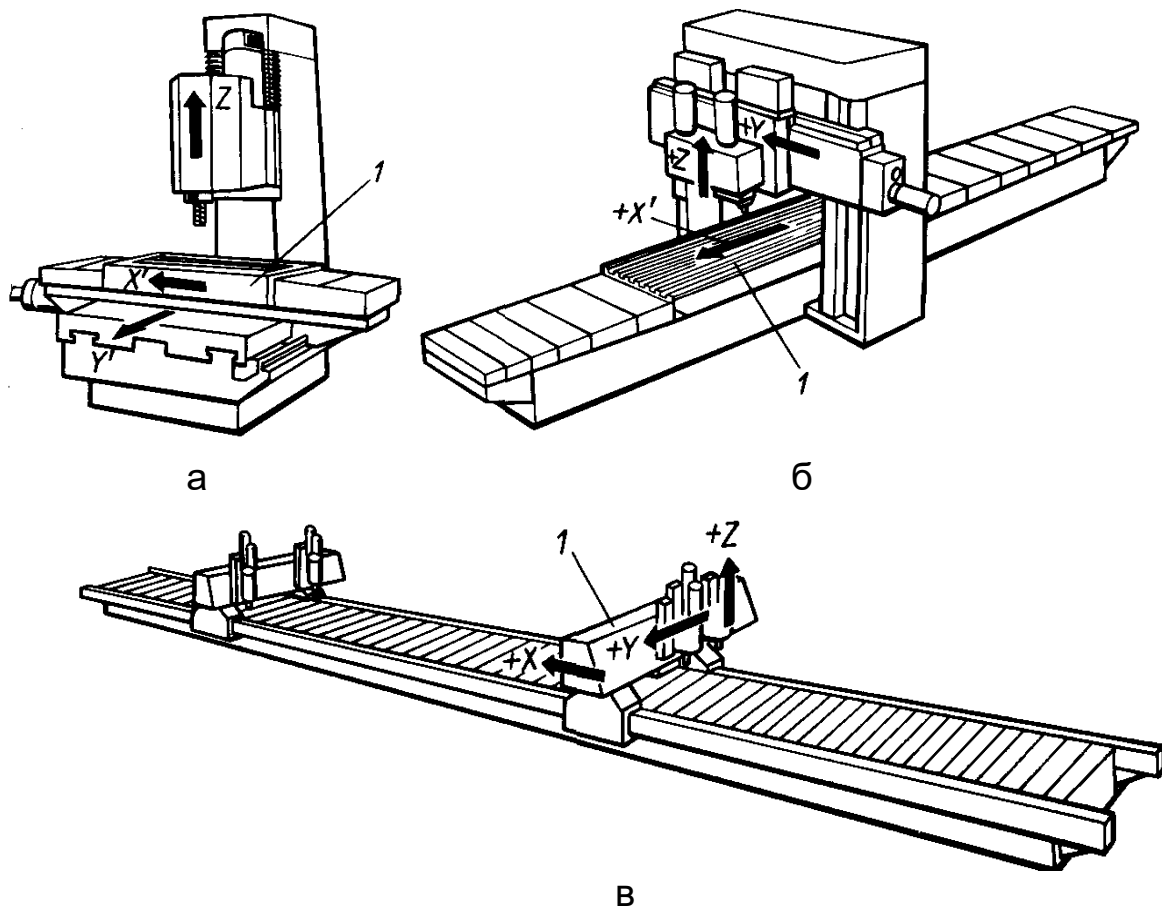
Базовые компоновки фрезерных станков с ЧПУ с различными ходами перемещений
